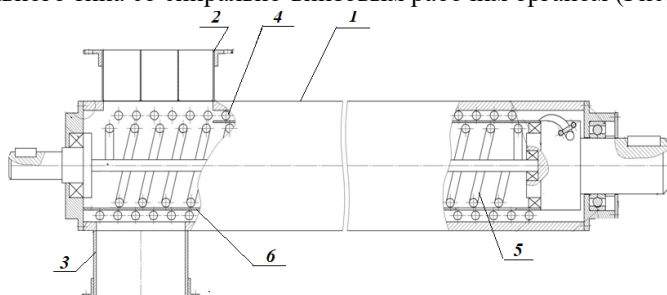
Предложенная конструкция смесителя непрерывного типа
